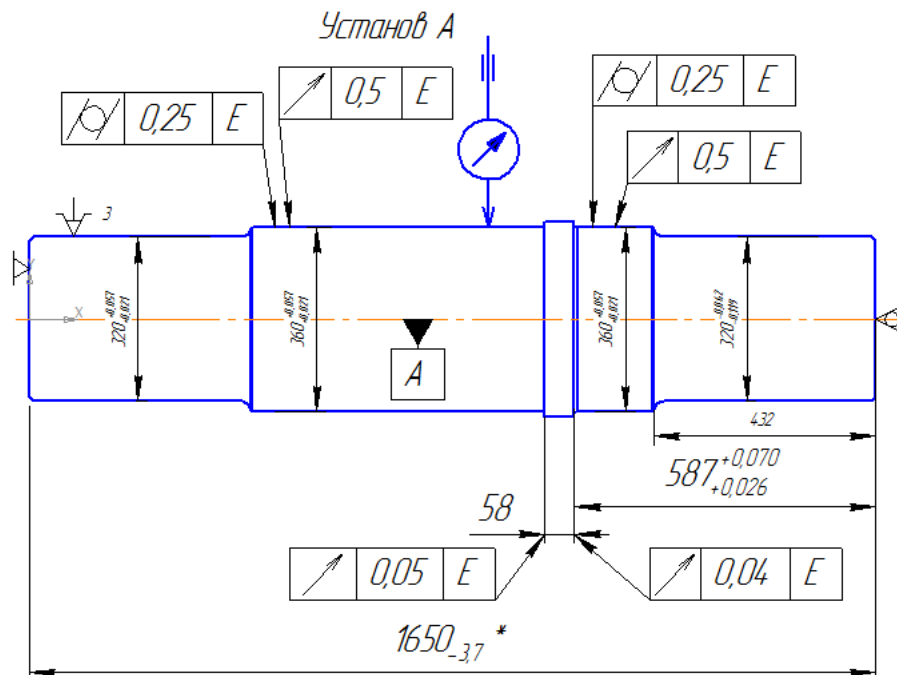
Схема базування деталі при виконанні контролю
